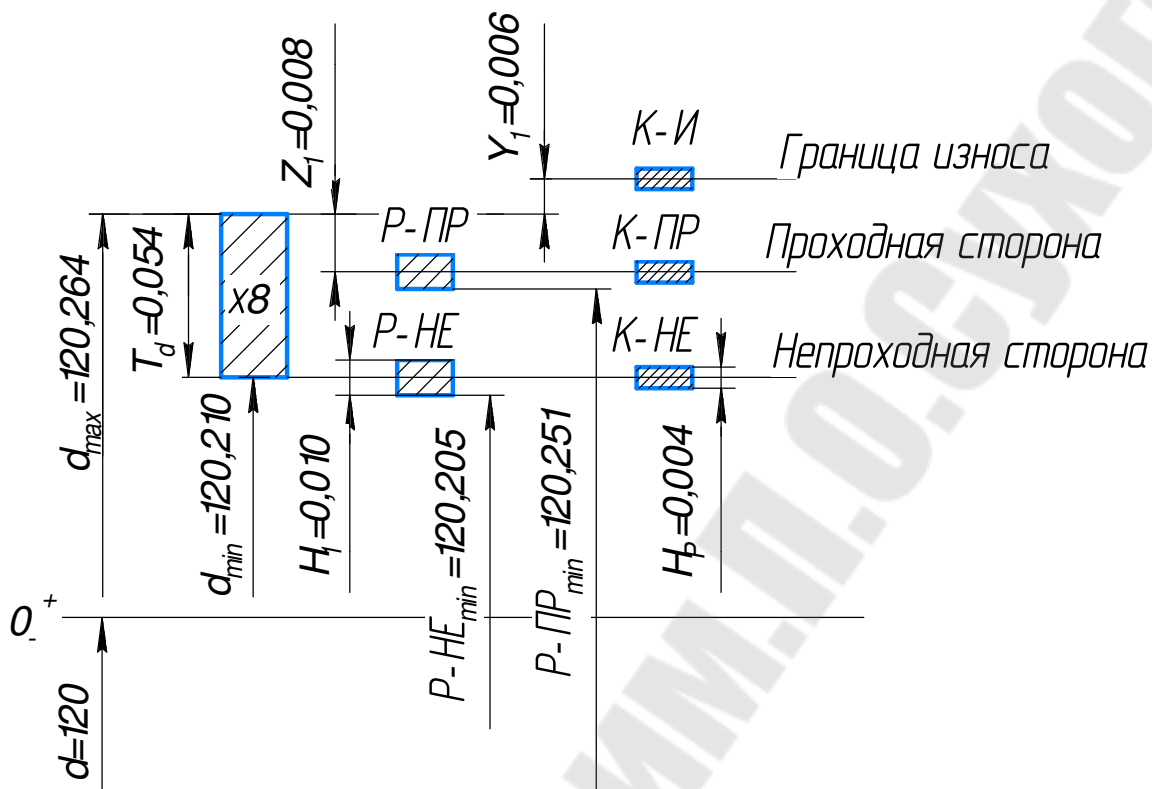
Схема расположения полей допусков рабочих и контрольных калибров
